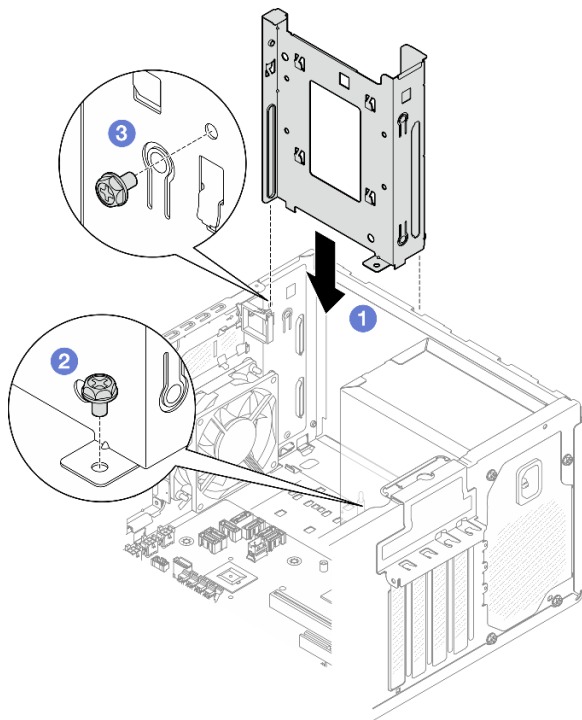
Installieren der Laufwerkhalterung für Position 0
